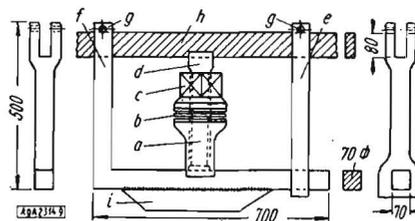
Vorrichtung zum Richten von Pflugrahmen
